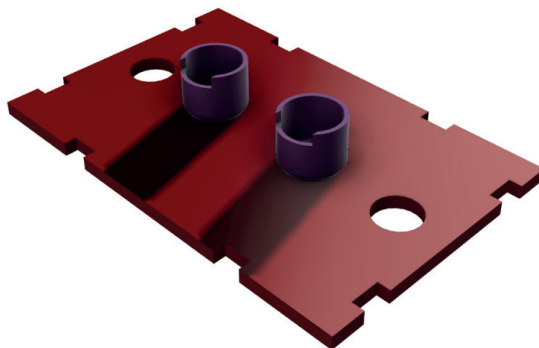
Conjunto da Tampa Interna (obtida por corte a laser) com o Suporte Inferior (obtido por impressão 3D).
